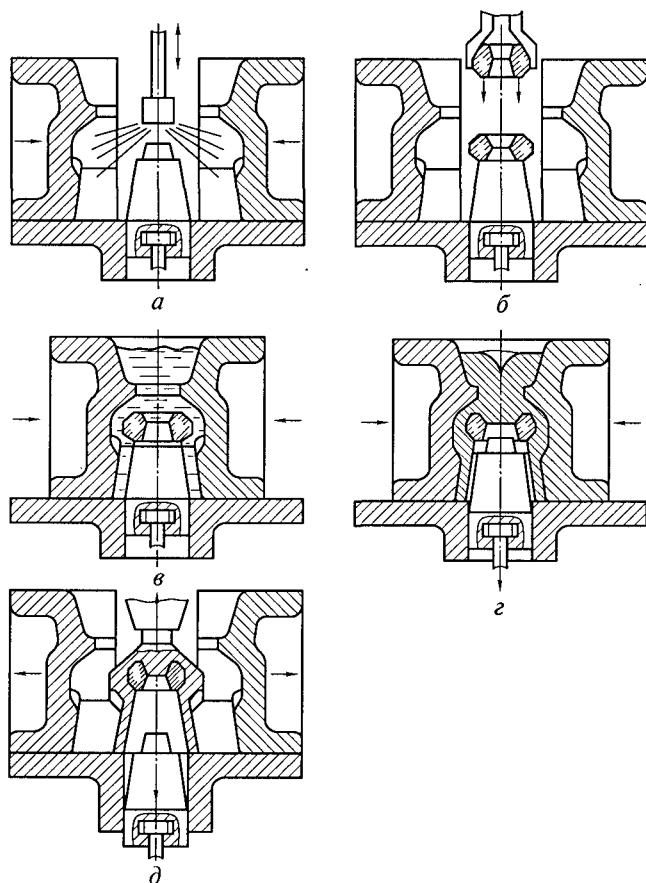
Последовательность изготовления отливки в кокиле (стрелки — направление движения деталей кокиля):
